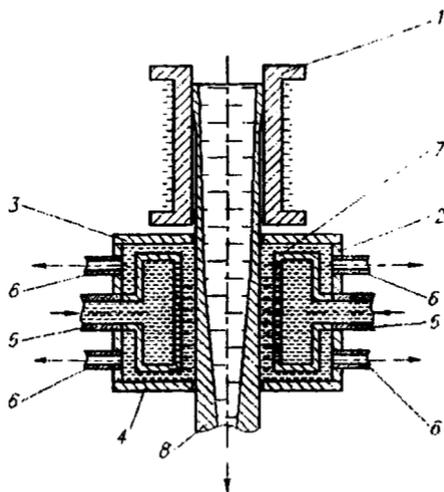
Схема устройства затопленно-струйного охлаждения непрерывнолитого слитка: 1 – кристаллизатор; 2 – кожух; 3 – фланец верхний; 4 – фланец нижний; 5 – патрубок подводящий; 6 – патрубок отводящий; 7 – коллектор; 8 – слиток
